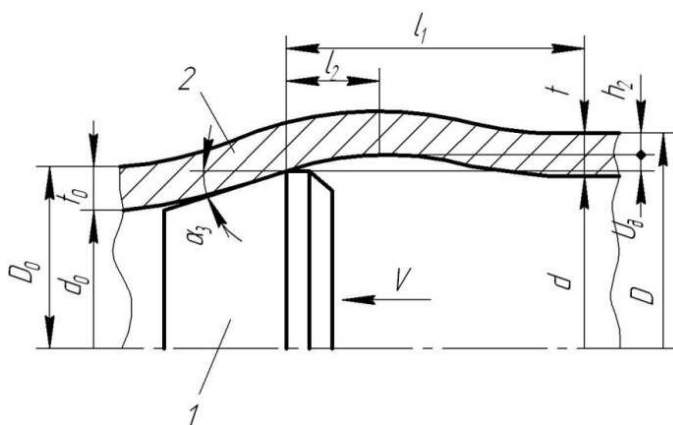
Схема контактной зоны при ДП полых трубчатых деталей 2 с конечной толщиной стенки деформирующим элементом 1: v – скорость протягивания; D_0 и D – соответственно внешние диаметры заготовки и детали после обработки; d_0 и d – соответственно диаметры отверстия заготовки и детали; t_0 и t – соответственно толщины стенки заготовки и детали; $2\alpha_z$ – угол заборного конуса ДЭ. Параметры ВВД: l_1 – длина; h_2 – высота; l_2 – расстояние от начала до максимума волны; U_δ – упругая усадка отверстия.
